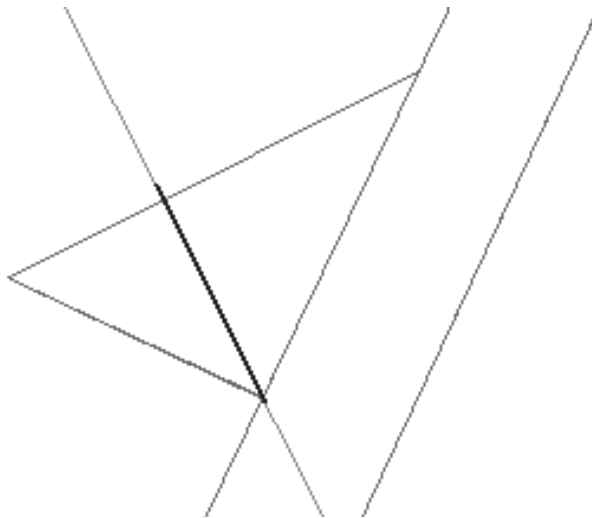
Ескіз для формування опорної поверхні під масловказівний покажчик
